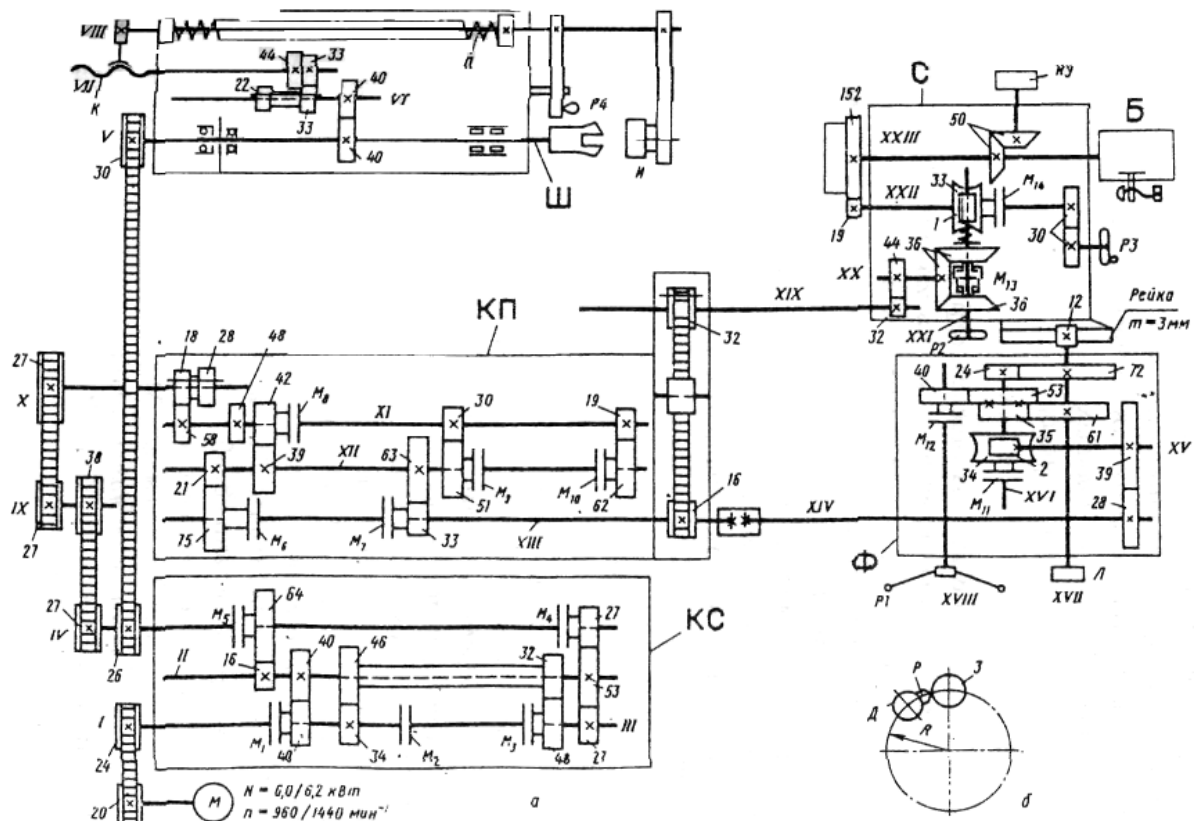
Кинематическая схема токарно-револьверного станка модели 1Г340
